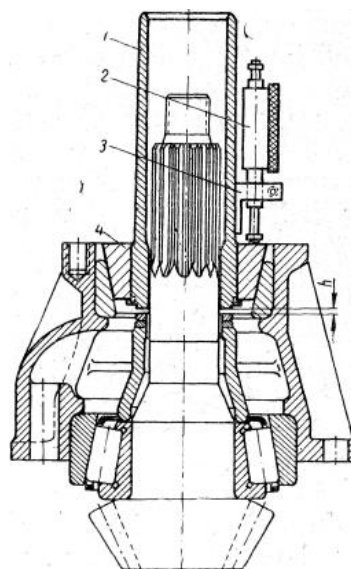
Пристосіблення для підбору комплекта регулювальних шайб підшипників вала ведучої конічної шестерні.
